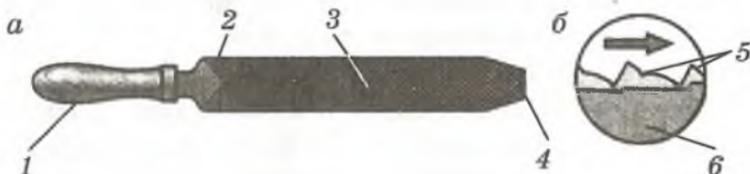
Напильник (а) и схема зачистки (б): 1 — ручка, 2 — стержень, 3 — насечка, 4 — носок, 5 — зубья, 6 — заготовка
